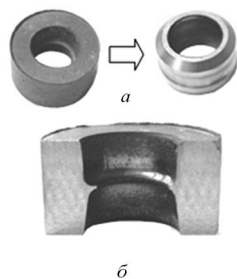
Рोलик дротого стану: а - поковка та ролік після її механічної обробки;
